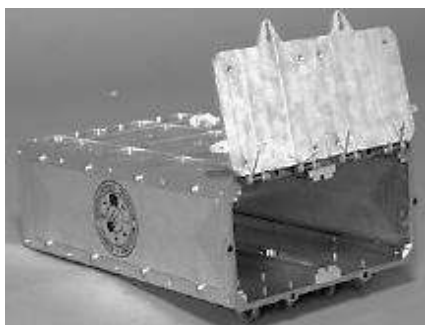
Изготовленный макет корпуса с механизмами ТПК для запуска МКА типоразмерностью от 1U до 3U
